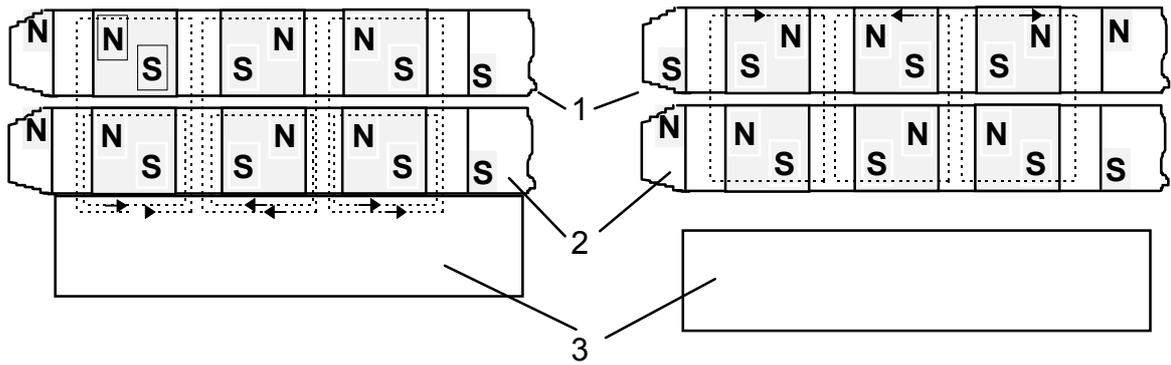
Принцип действия грузозахватного приспособления: 1 - подвижный магнитный блок; 2 - неподвижный магнитный блок; 3 - деталь.
